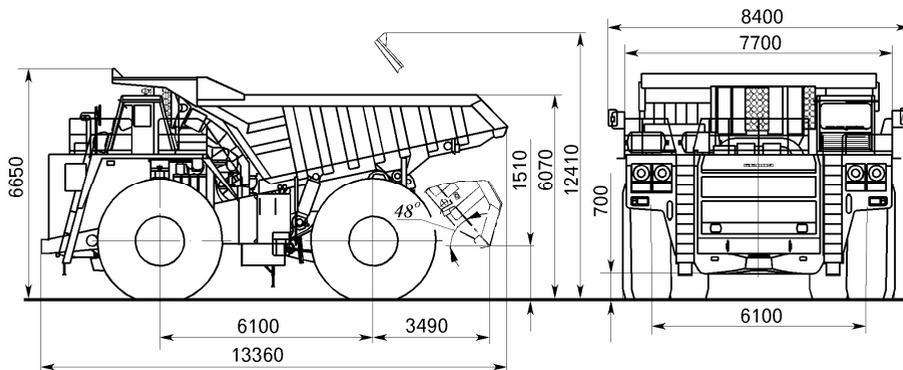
Карьерный самосвал БелАЗ-75306. Габаритные размеры
